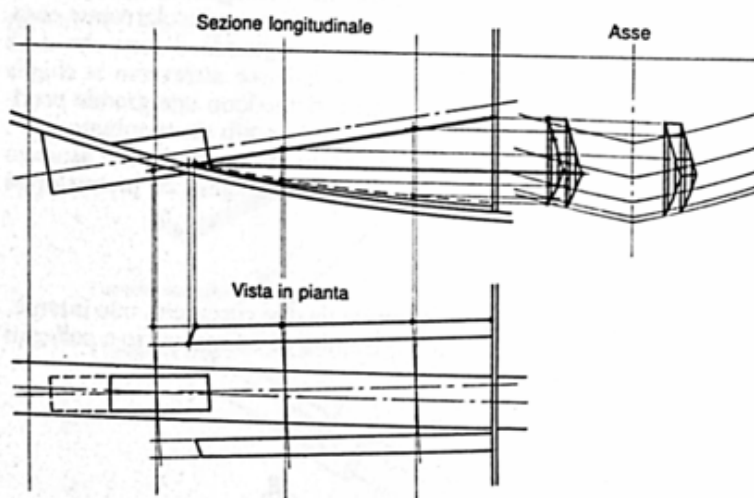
Esempio di tracciato complesso dei paramezzali con linea d'asse inclinata trasversalmente. Nella sezione longitudinale si vede soltanto il paramezzale di dritta; le linee di riferimento corrispondono al suo lato esterno.
